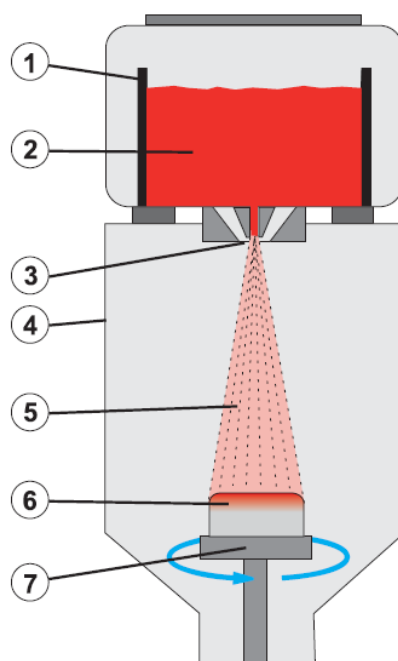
Схема получения заготовок для производства заливаемых алюминиевых гильз по технологии Silitec: 1 – литейный тигель, 2 – расплав, 3 – кольцевое сопло, 4 – камера набрызгивания, 5 – конус набрызгивания, 6 – заготовка, 7 – вращающаяся тарелка [21]
